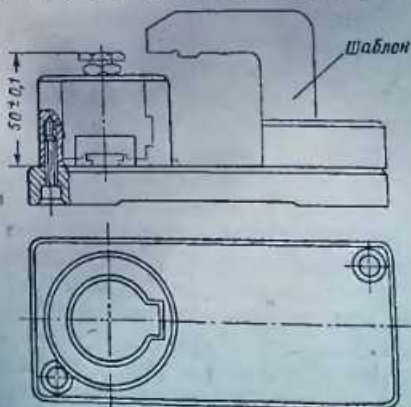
Приспособление ЛМ9690-379 с шаблоном ЛМ9557-379 для установки регулировочного болта толкателя
